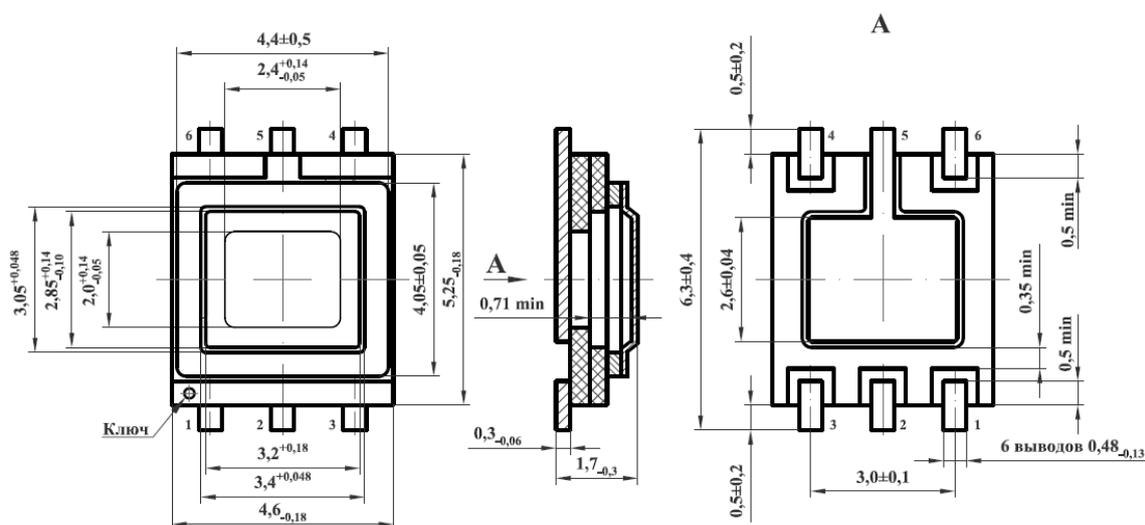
Габаритный чертёж корпуса 5221.6-1 (размеры в мм)
